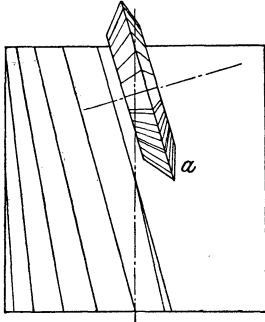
Das Fräsen spiral­gewundener, geriefter Fräser.
